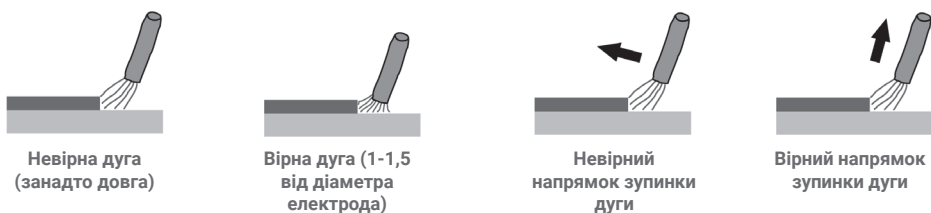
Відстань розташування електрода із покриттям до деталі під час ручного дугового зварювання («ММА»).
